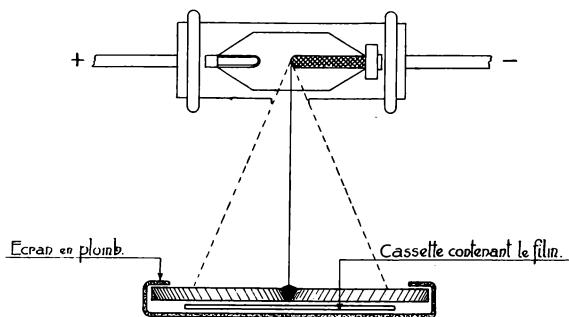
Vue schématique de la radiographie d'un cordon de soudure.
